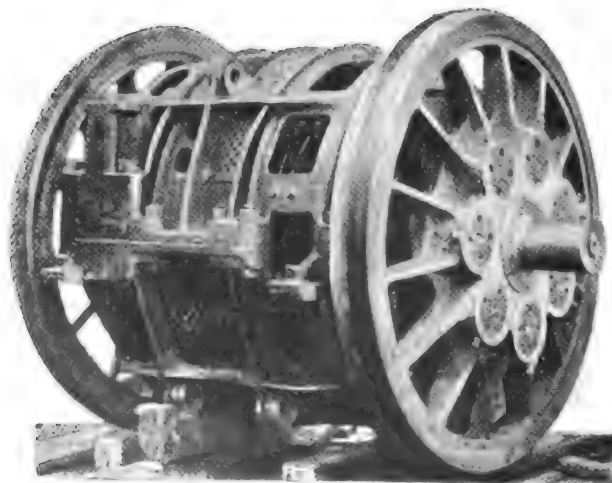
Vue d'un moteur complet en place sur l'essieu.
